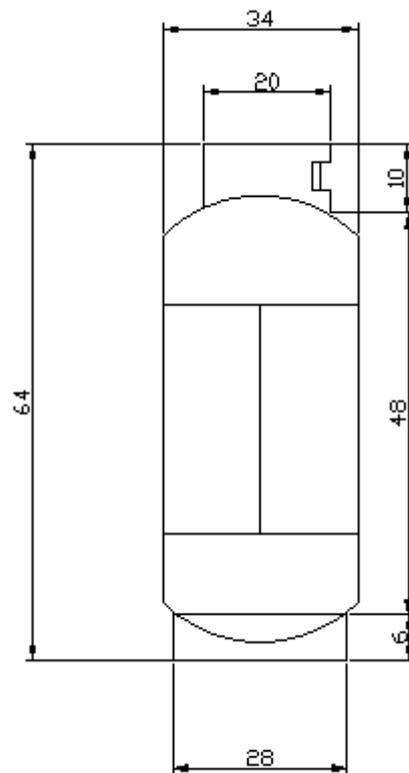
DIMENSIONES DEL CILINDRO GLP
